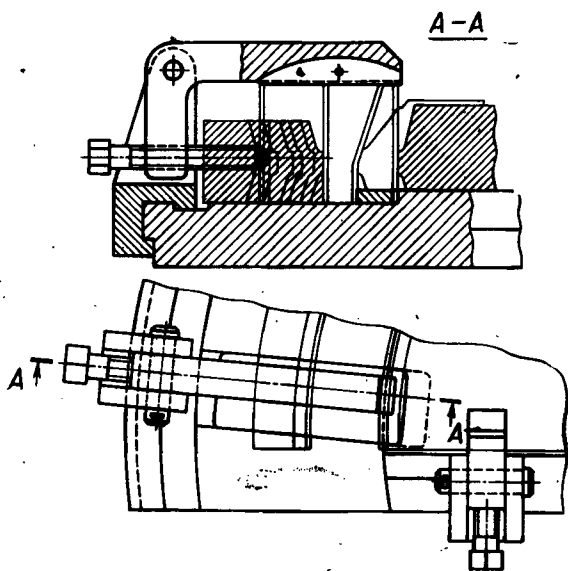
Приспособление для сборки диафрагмы под сварку
